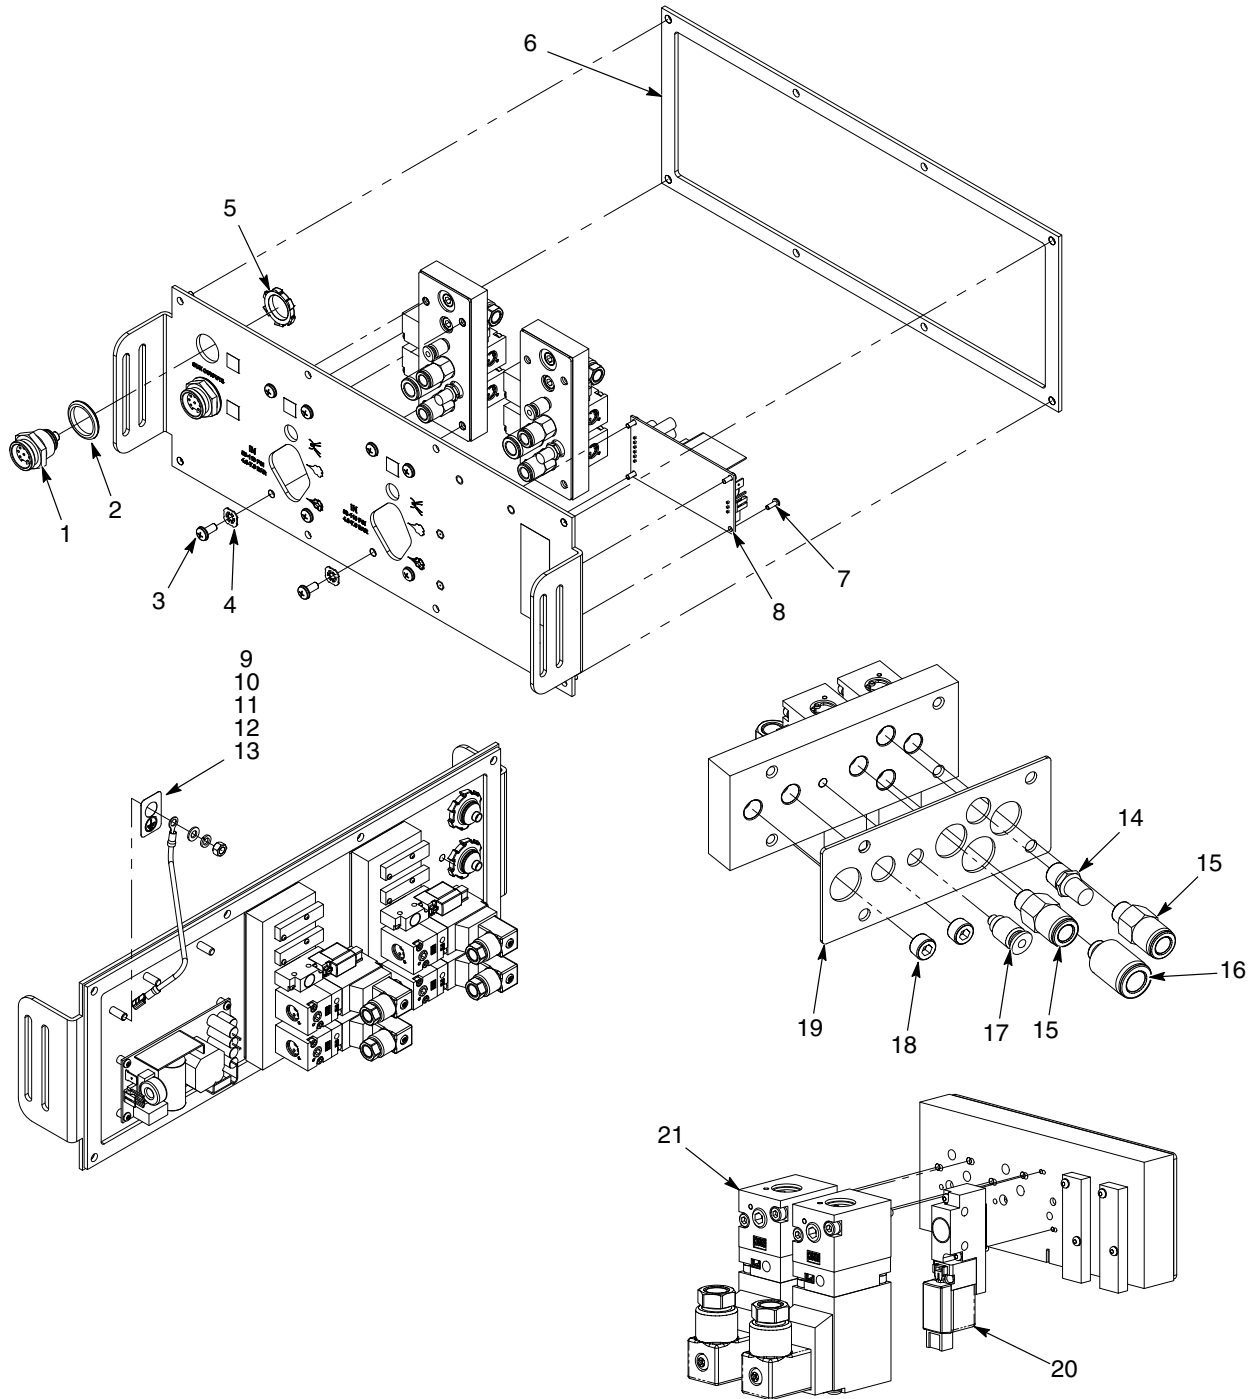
Unterbaugruppe Rückwand - Doppelpistolensteuerung und Steuerung für mehrere Pistolen
